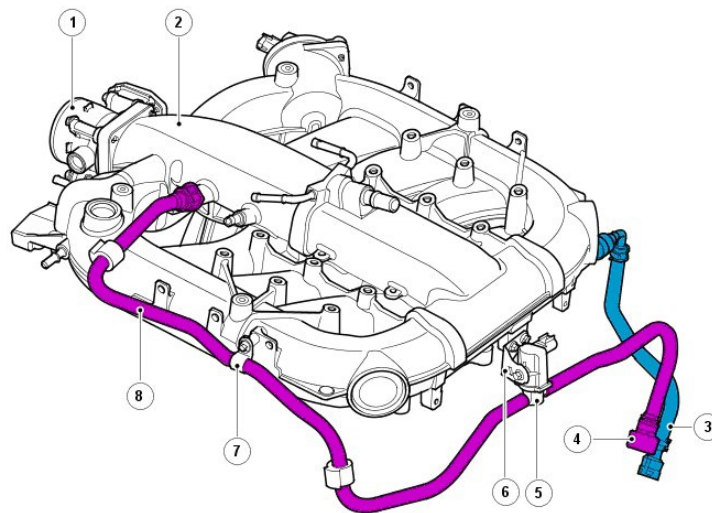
Клапан продувки и шланги бензинового двигателя 4.0L V6
